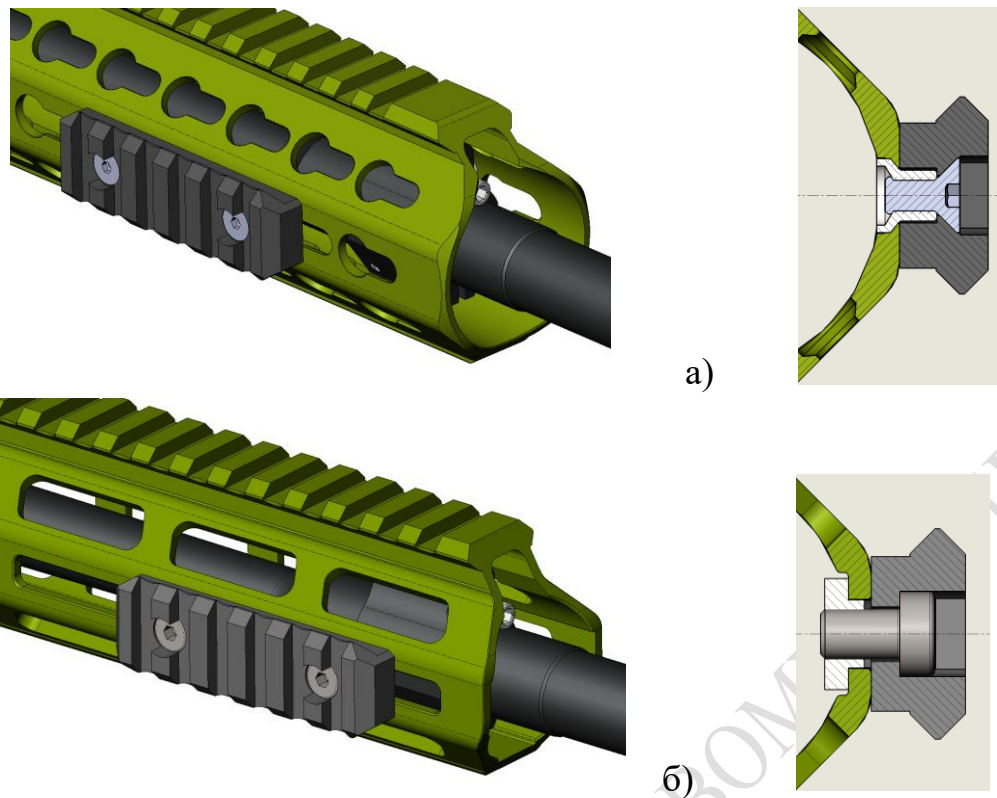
Кріплення планки Пікатінні на цівку з кріпленням типу:
